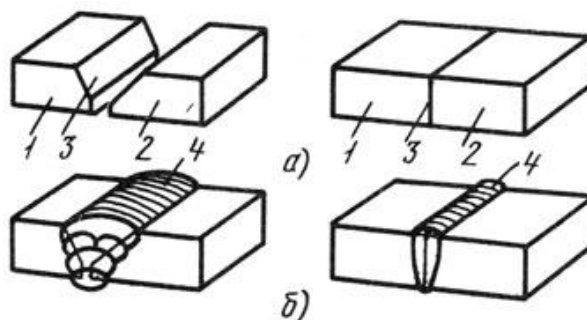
Схема соединения деталей сваркой плавлением: а - детали перед сваркой, б - детали после сварки
